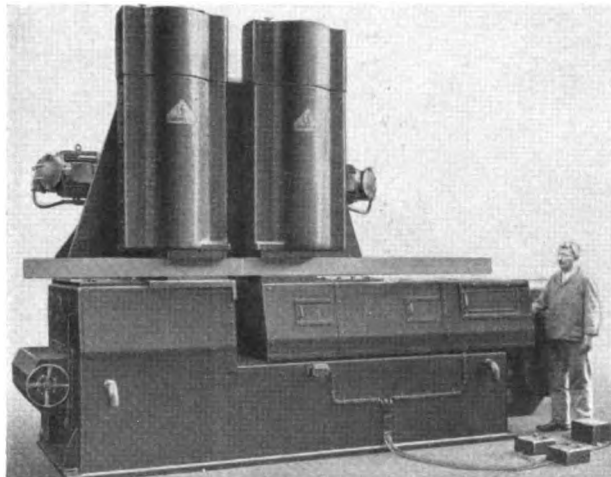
Selbsttätige Stumpfschweißmaschine, vorwiegend zum Schweißen von Eisenbahnschienen.
